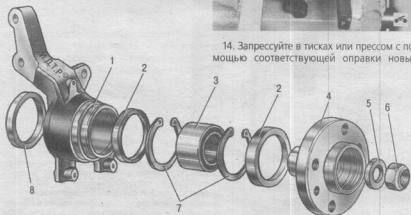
Поворотный кулак и детали ступицы переднего колеса: 1 – поворотный кулак; 2 – наружное граэстоотражательное кольцо; 3 – подшипник ступицы; 4 – ступица колеса; 5 – упорная шайба; 6 – гайка; 7 – стопорные кольца; 8 – внутреннее граэстоотражательное кольцо
